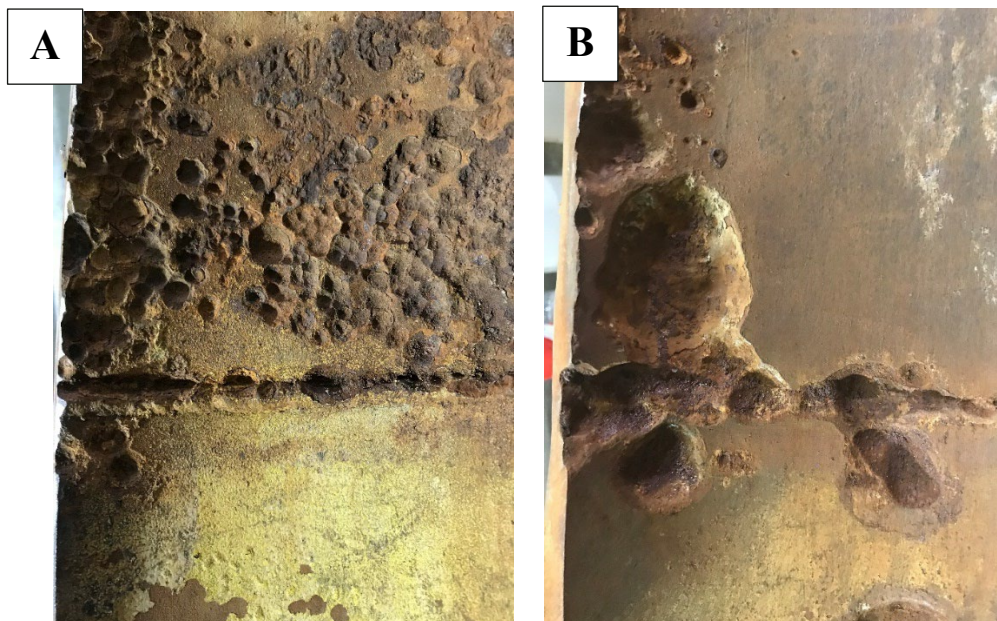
Pittings de corrosión. Ataque preferencial sobre el caño y la soldadura.
